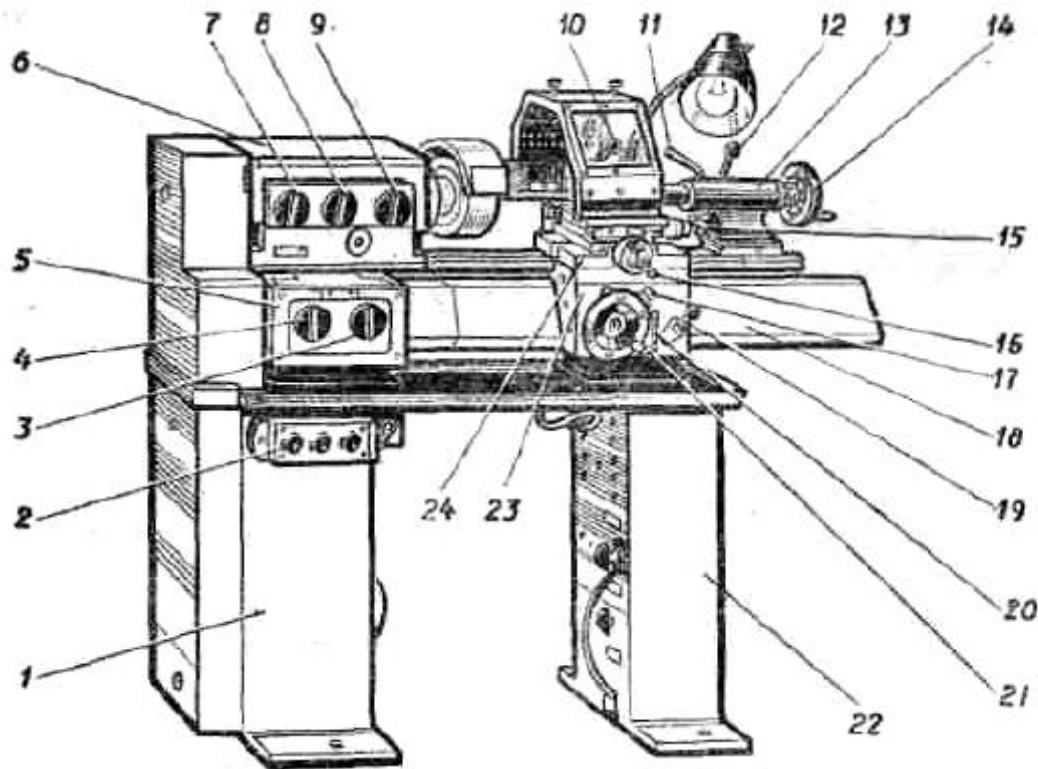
Токарно-гвинторізний верстат ТВ-6 1 - передня тумба; 2 - кнопочний пост управління; 3 - рукоятка включення ходового валика та ходового гвинта; 4 - рукоятка установки величини подачі і шага різьби; 5 - коробка подачі; 6 - передня бабка; 7 - рукоятка зміни напрямку подачі; 8 і 9 - рукоятки установки частоти обертання шпинделя; 10 - рукоятка кріплення різцевої головки; 11 - рукоятка кріплення пінолі задньої бабки; 12 - рукоятка кріплення задньої бабки до напрямних станини; 13 - задня бабка; 14 - маховик пересування пінолі задньої бабки; 15 - рукоятка ручного переміщення верхніх полозок супорта; 16 - рукоятка пересування поперечних полозок; 17 - кнопка ввімкнення та вимкнення рейкової шестерні; 18 - станина; 19 - рукоятка ввімкнення гайки ходового гвинта; 20 - рукоятка ввімкнення повздовжньої механічної подачі; 21 - маховик ручної повздовжньої подачі; 22 - задня тумба; 23 - фартух; 24 - супорт.
